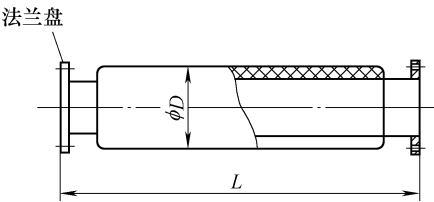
33 ADS 出气口消声器（立式用）外形尺寸
